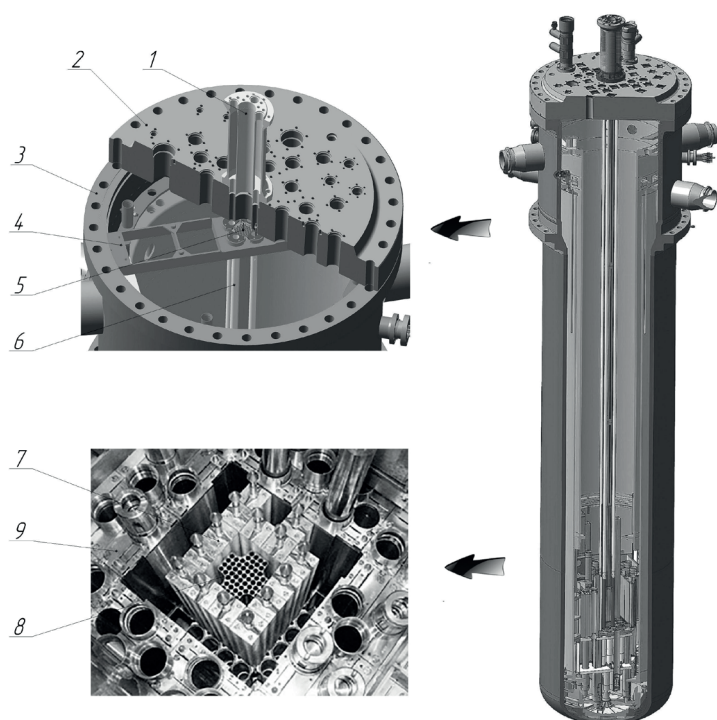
Вертикальный разрез реактора; крышка и вид новой активной зоны: 1 – центральный стояк; 2 – крышка реактора; 3 – корпус реактора; 4 – установочная плита; 5 – нейтронная ловушка; 6 – направляющая труба РО АЗ-КО; 7 – ТВС; 8 – хвостовик нейтронной ловушки; 9 – бериллиевые блоки отражателя
